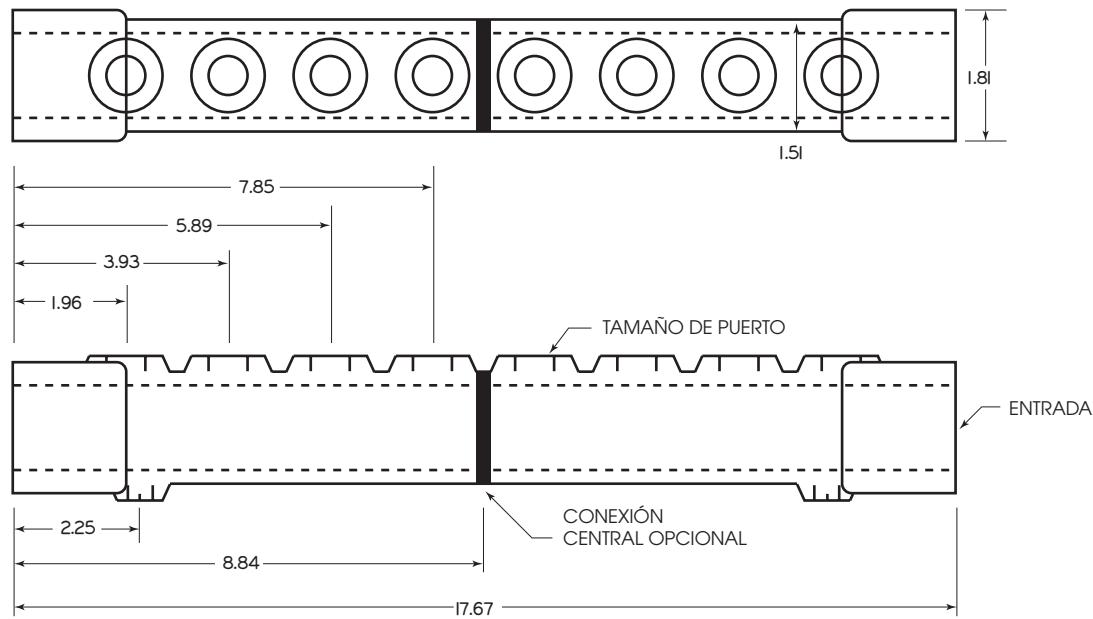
■ Proy. 13.50. Distribuidor de nylon de 8 puertos. Dibuje las vistas inferior e izquierda. Rediseñe con dimensiones métricas.
